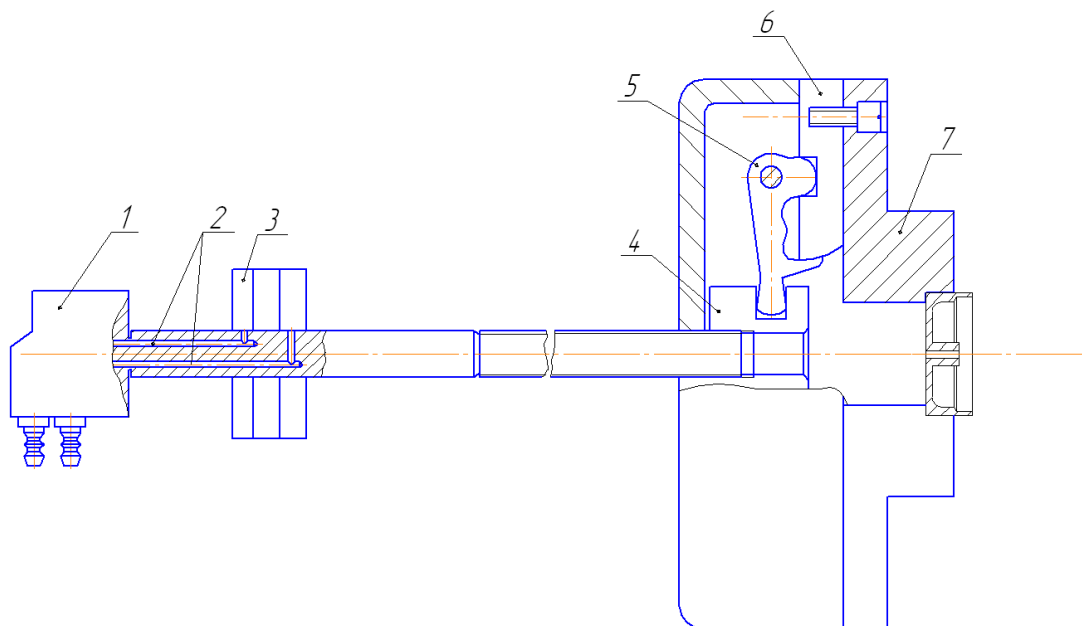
Трехкулачковый патрон с пневмоприводом
